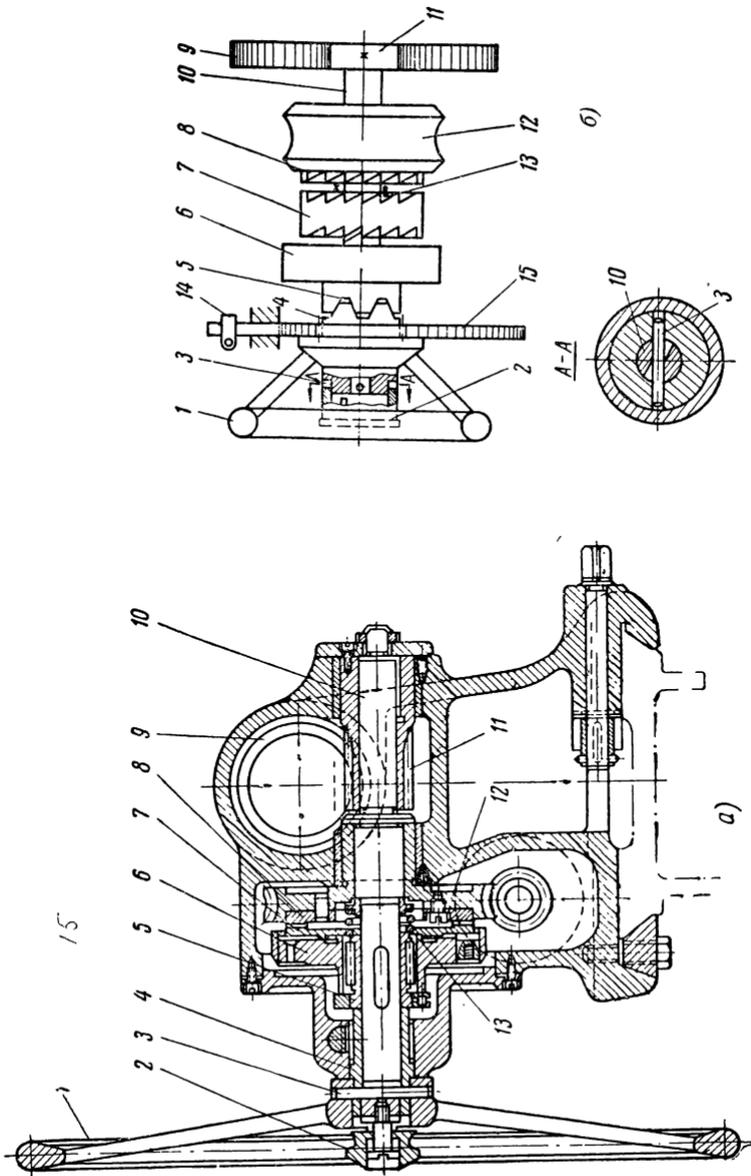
Механизм включения и выключения подачи шпинделя вертикально-сверильного станка
